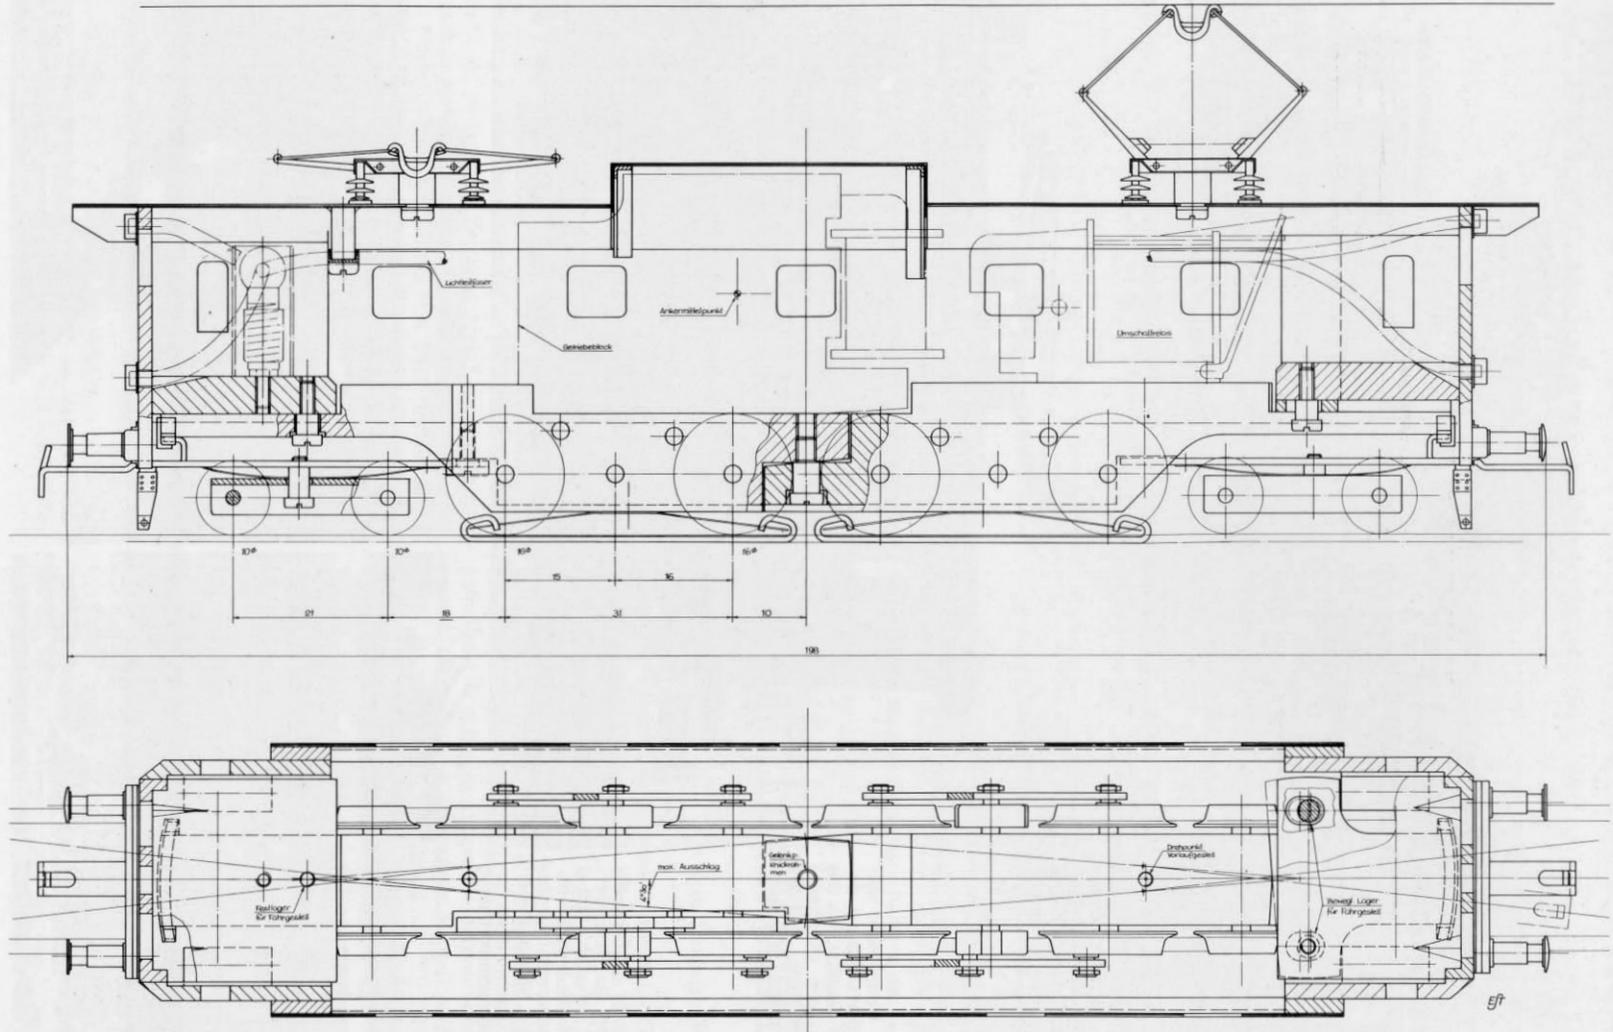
An dieser selbstgefertigten Bauzeichnung (wiedergegeben in 1/1 H0-Größe, Maßstab 1 : 87) orientierte sich der Erbauer. So sieht man z. B. die Lage des Getriebe-/Motorblocks, die Befestigungsschrauben von Gelenkrahmen und Vorlaufgestellen oder die Position der Lichtleitkabel.
